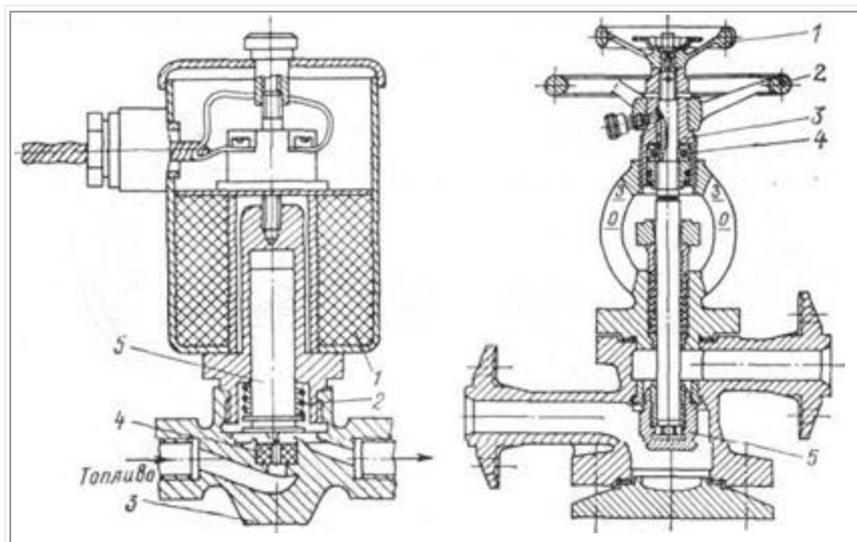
Электромагнитный быстрозапорный топливный клапан
